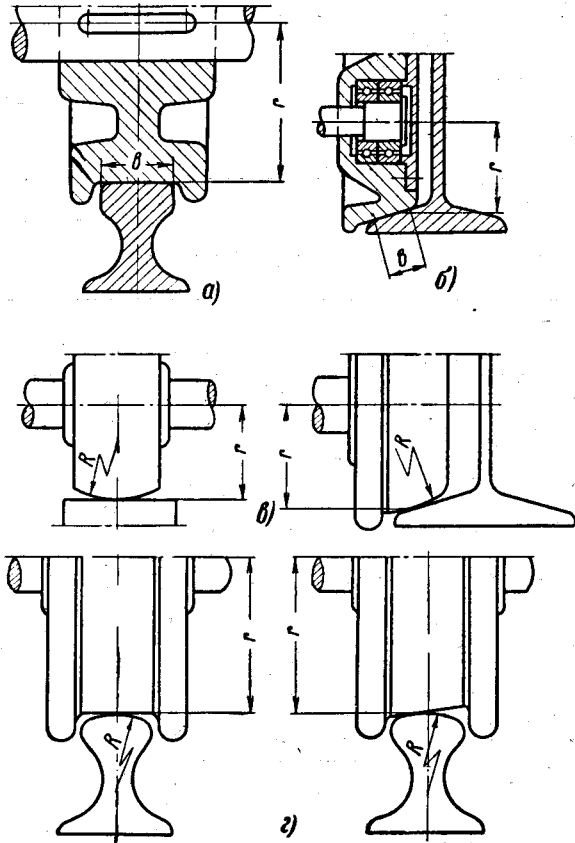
Профили обода катка и головки рельса. а — цилиндрический обод с плоской головкой рельса; б — конический обод с наклонной поверхностью рельса; в — обод с выпуклой поверхностью на плоской поверхности головки рельса; г — цилиндрический и конический ободья с выпуклой головкой рельса.
